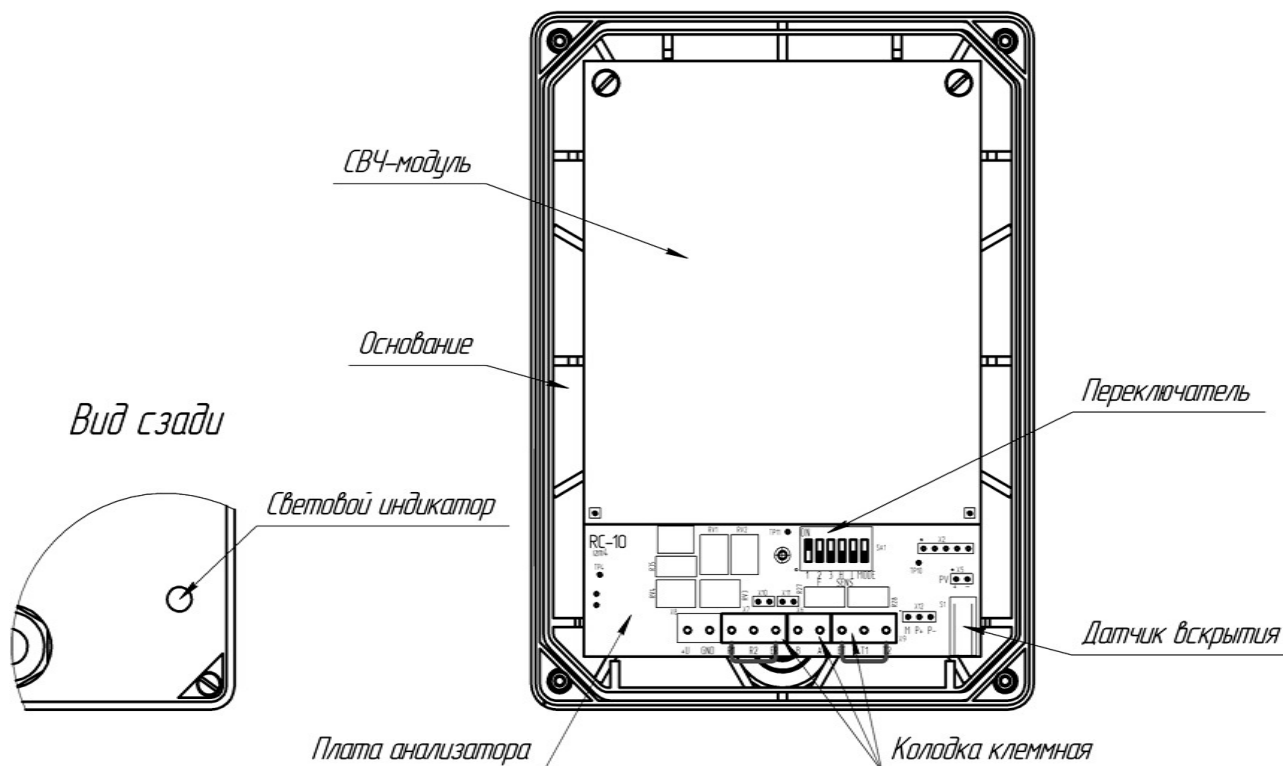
Внешний вид блока ПРМ со снятой крышкой
